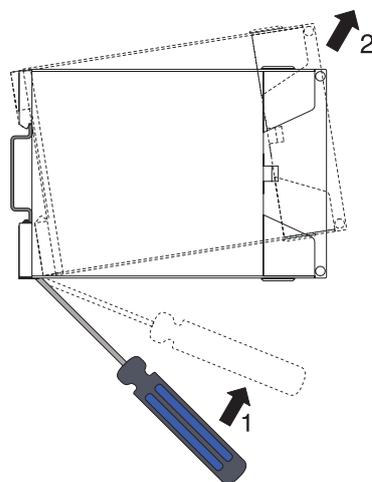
Демонтаж барьеров ЭНИ-БИС-101...111, 117-Ех с DIN-рейки
